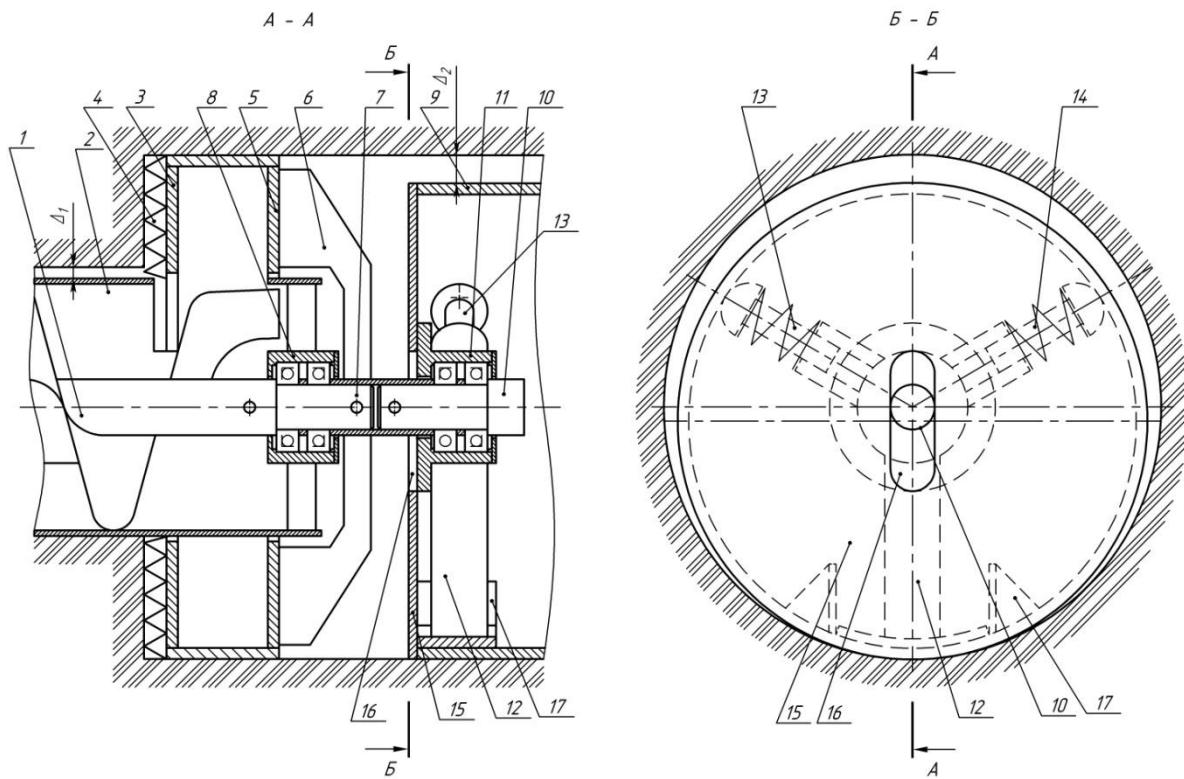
Расширитель обратного хода с якорно-прицепным устройством:
